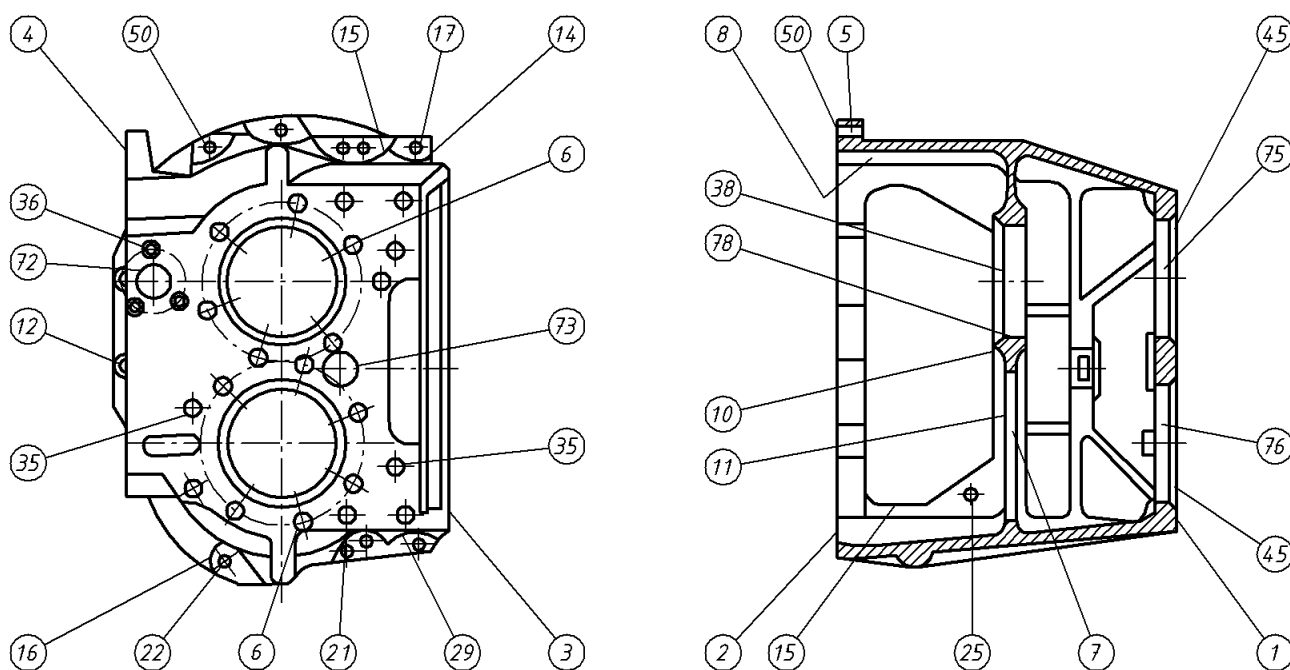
Картер коробки передач 695Ж2-1701015-В
